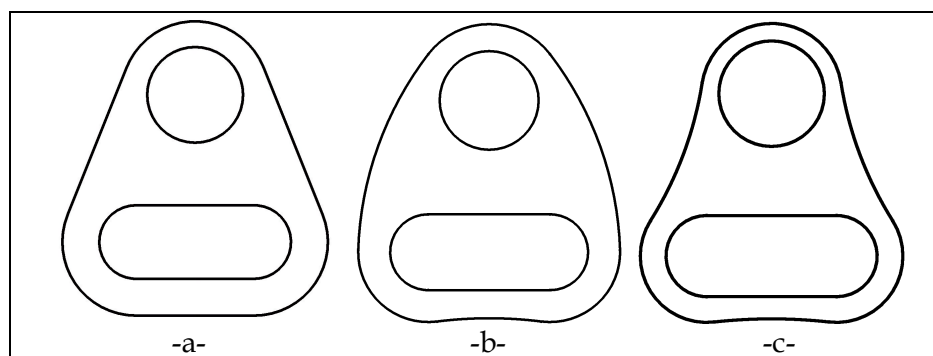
Schéma des pièces étudiées -a- pièce actuelle -b- pièce de la première génération -c- pièce sur le front de Pareto
